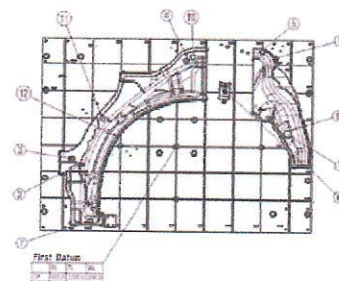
Pengukuran untuk Datum Hole No. 5
